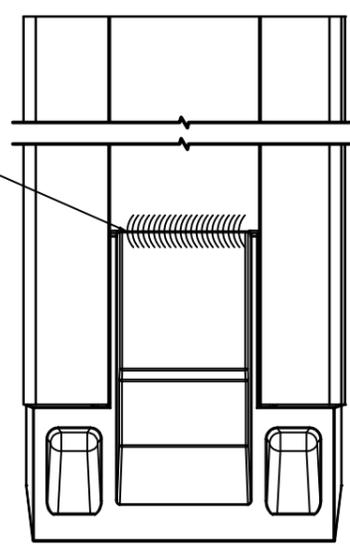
EMBOUT EN ALUMINIUM INSTALLATION VUE DE DESSOUS
